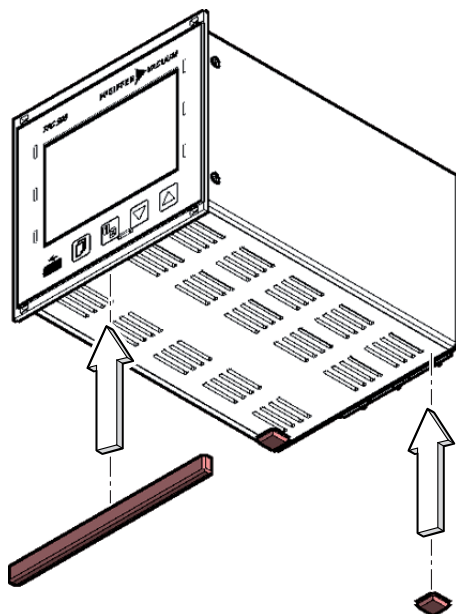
Закрепление резиновых ножек и резиновой полоски
